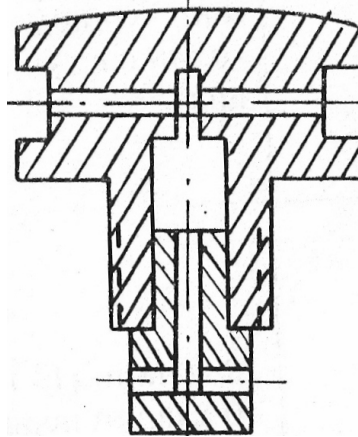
Робоча пробка свинцево-кислотного акумулятора
